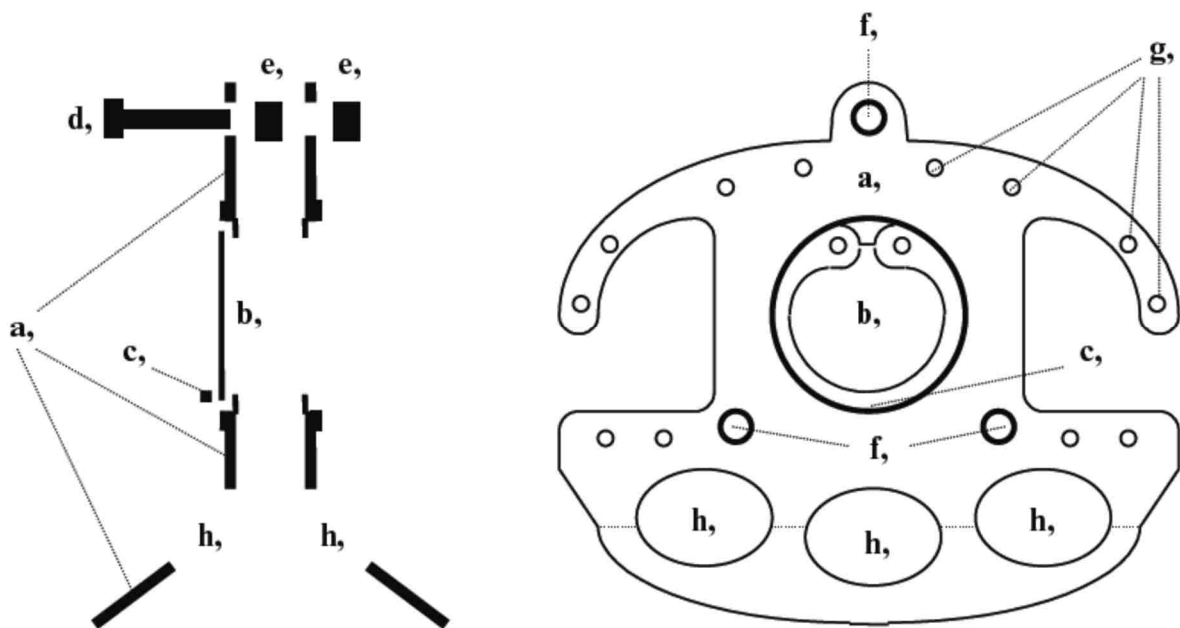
Technische Zeichnung der Rückenhautkammer. (A) Schnitt durch die Mitte der Rückenhautkammer, (B) Seitliche Ansicht. a Titanrahmen, b Deckglas, c Sprengring, d Schraube, e Mutter, f Bohrlöcher für die Schrauben, g Bohrlöcher für die Fixationsnähte, h Aussparungen zur Gewichtsreduktion der Kammer (77).
